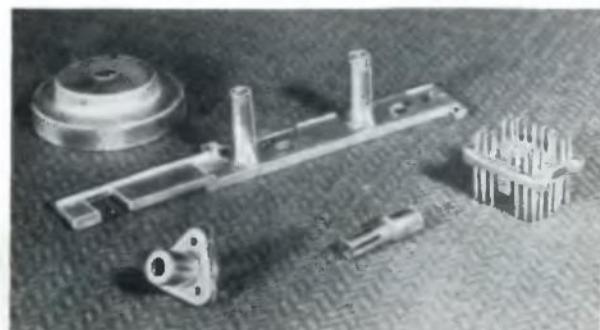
Детали для магнитофона, изготовленные литьем под давлением из цинкового (ЗАМ4-1) и алюминиевого (А.Л2) сплавов
